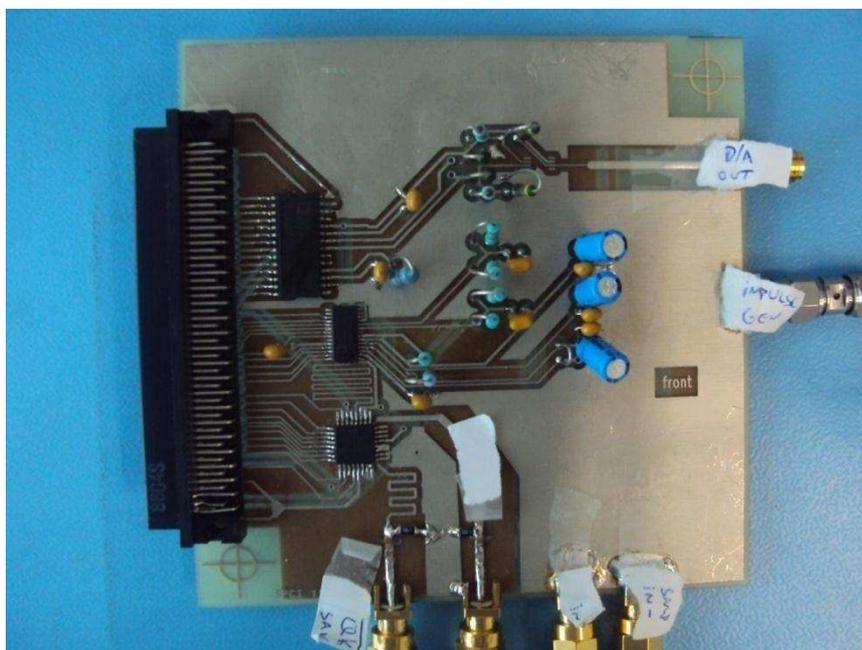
(a) – Circuito impresso desenvolvido com KiCAD, fabricado pela empresa CIRE e soldado no laboratório LCIS (frente).
